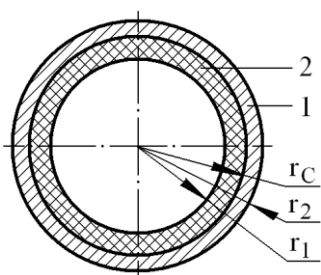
Схема поперечного сечения цилиндрической отливки с полым стержнем:
